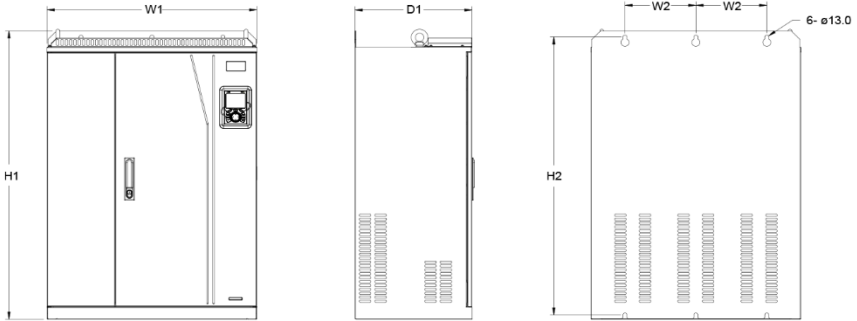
Схема настінного монтажу ПЧ напругою 380 В, потужністю від 220 до 315 кВт
